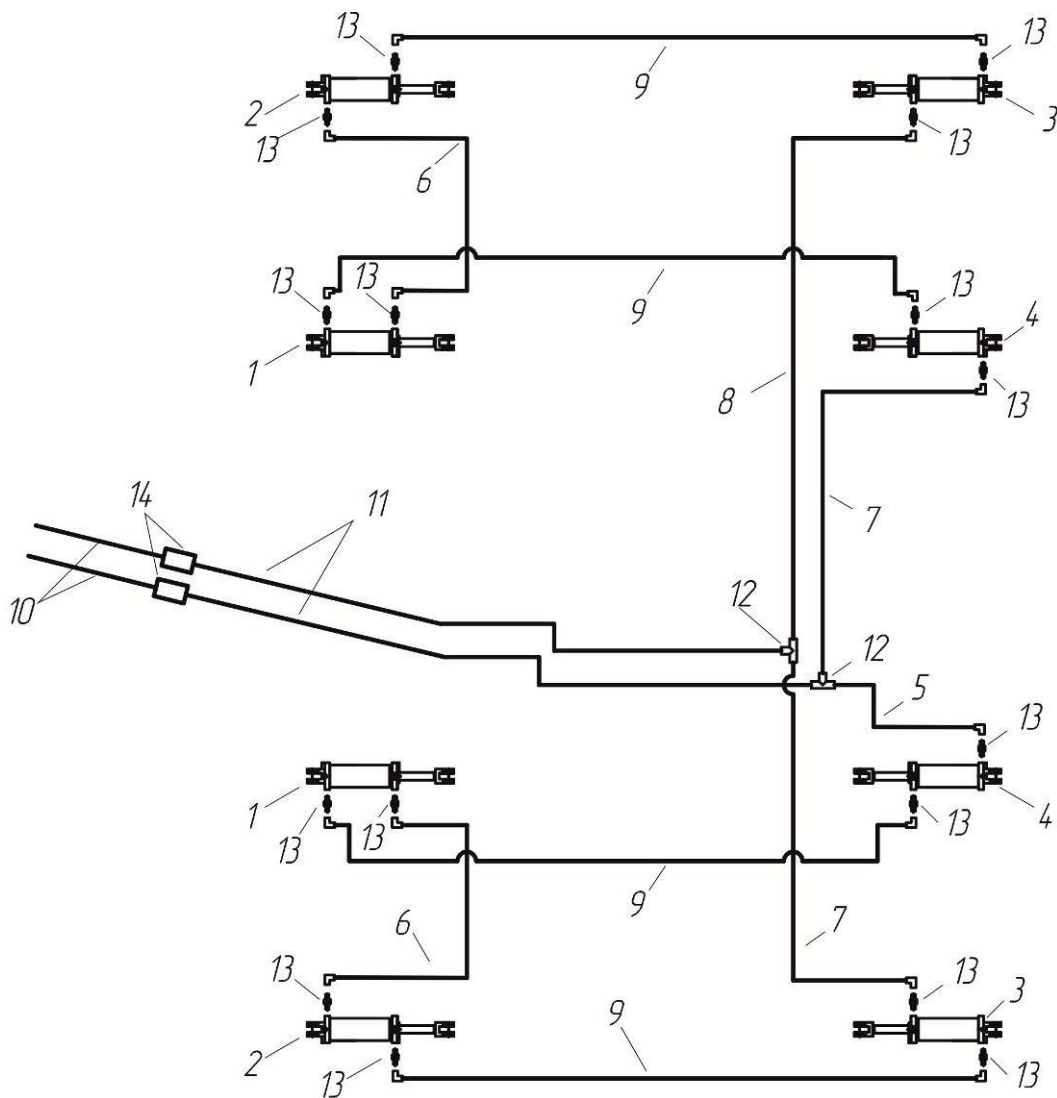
Схема установки гидроцилиндров и шлангов ПК-6.1К
